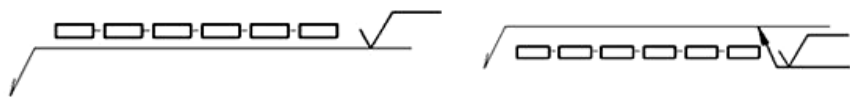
Обозначение шероховатости механически обработанной поверхности шва
